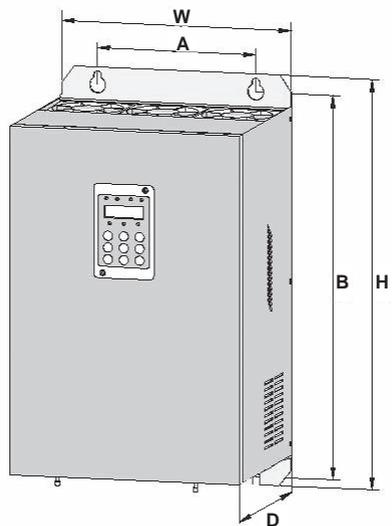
Внешний вид и тип монтажа преобразователя частоты в металлическом корпусе
